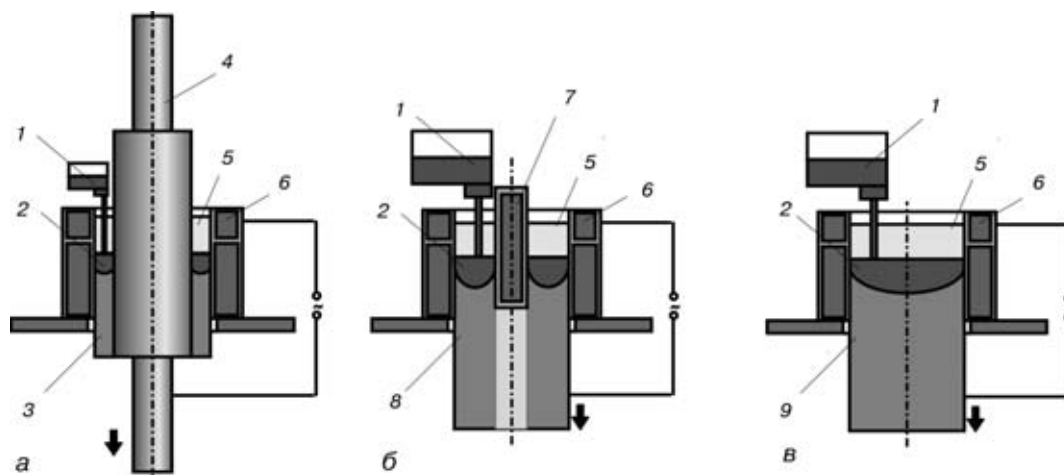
Схемы реализации процесса ЭШП с жидким металлом: при наплавке прокатных валков (а), выплавке полых слитков (б) и электрошлаковым непрерывном процессе получения слитков сплошного сечения (в): 1 — устройство для заливки исходного (присадочного) жидкого металла; 2 — металлическая ванна; 3 — наплавленный слой; 4 — прокатный валок; 5 — шлаковая ванна; 6 — токоподводящий водоохлаждаемый кристаллизатор; 7 — дорн для формирования внутренней полости слитка; 8 — полый слиток; 9 — слиток сплошного сечения
